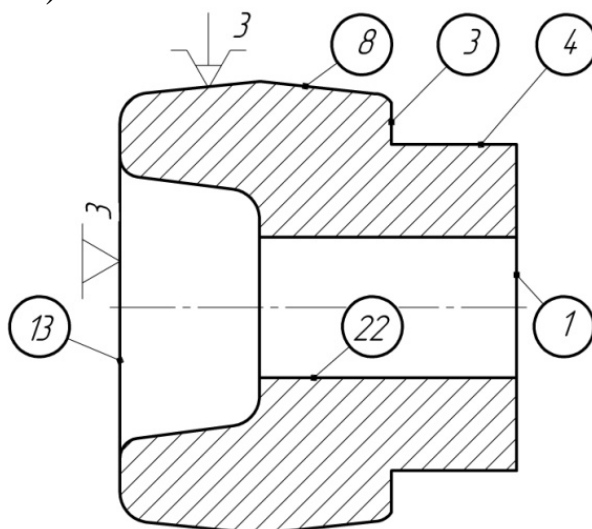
Схема базирования заготовки на установе А операции 005
